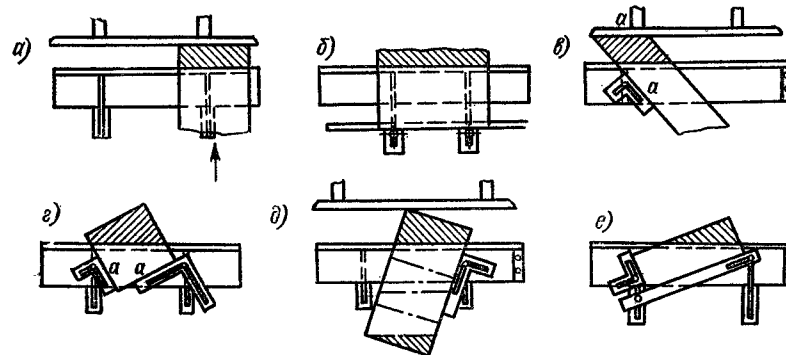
Резка штучных заготовок на гильотинных ножницах
